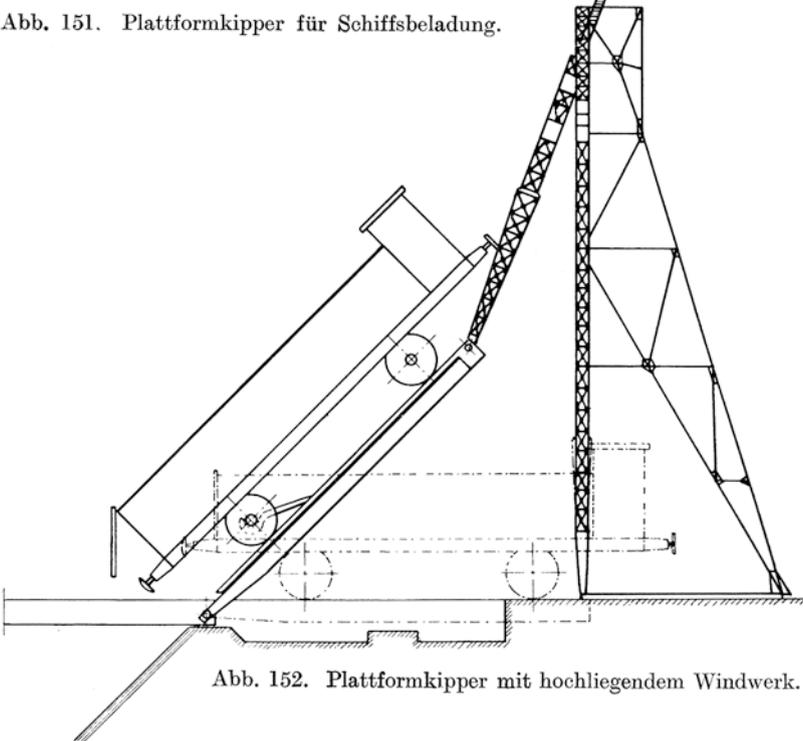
Plattformkipper mit hochliegendem Windwerk.
